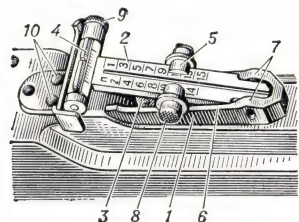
Прицел 7,62-мм пулемёта Калашникова: 1 — колющая планка; 2 — прицельная планка; 3 — пластинчатая пружина; 4 — целик; 5 — хомут; 6 — сектор колодки; 7 — проушина; 8 — защёлка хомута; 9 — маховик винта целика; 10 — предохранитель целика.
